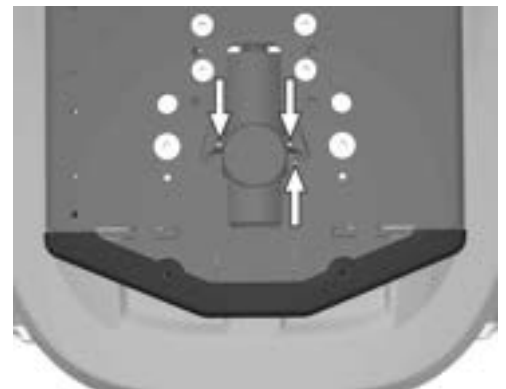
Der Elektromotor für den Sitzneigungsmechanismus wird mit drei Schrauben montiert.
